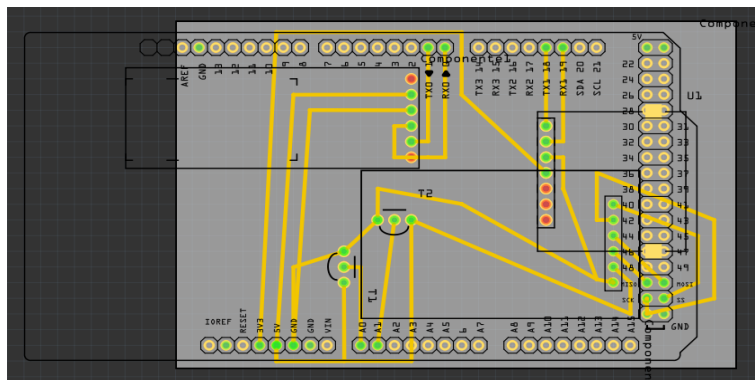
Diseño de la Placa PCB de la Shield en Fritzing Fab.
